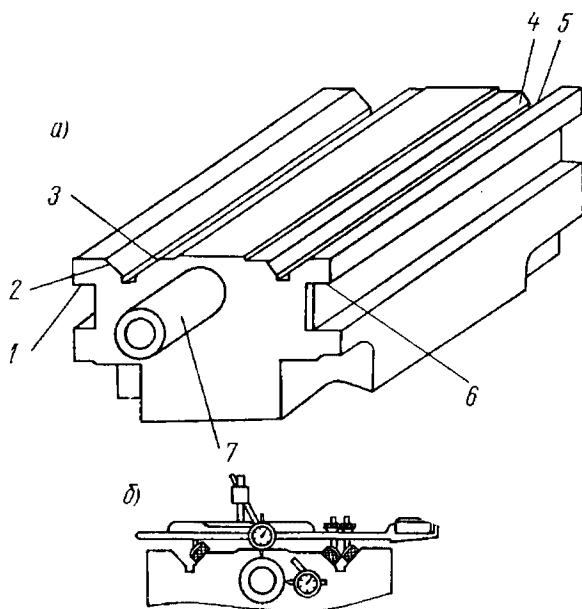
Корпус шпиндельного узла: а — общий вид; б — схема проверки
